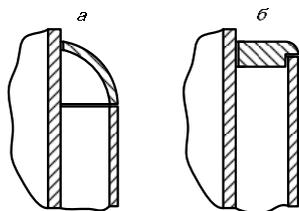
Способы приварки рубашки к корпусу аппарата: а – с помощью отбортовки; б – с помощью приварного кольца.
